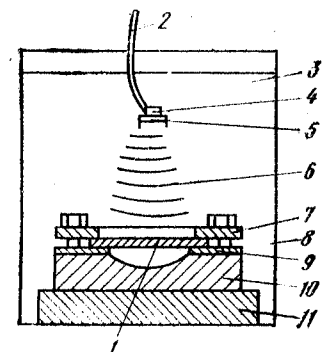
Принципиальная схема установки для штамповки взрывом: 1 — заготовка; 2 — провода; 3 — вода; 4 — детонатор; 5 — заряд; 6 — взрывные волны; 7 — прижимное кольцо; 8 — бак; 9 — прокладка; 10 — матрица; 11 — основание
